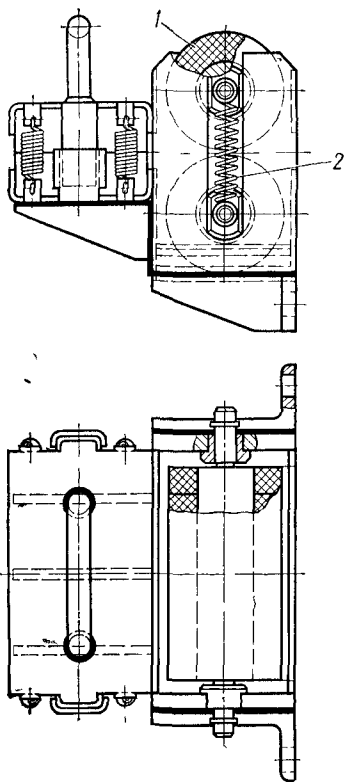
Устройство с вращающимися кольцами для очистки и смазывания ленты
